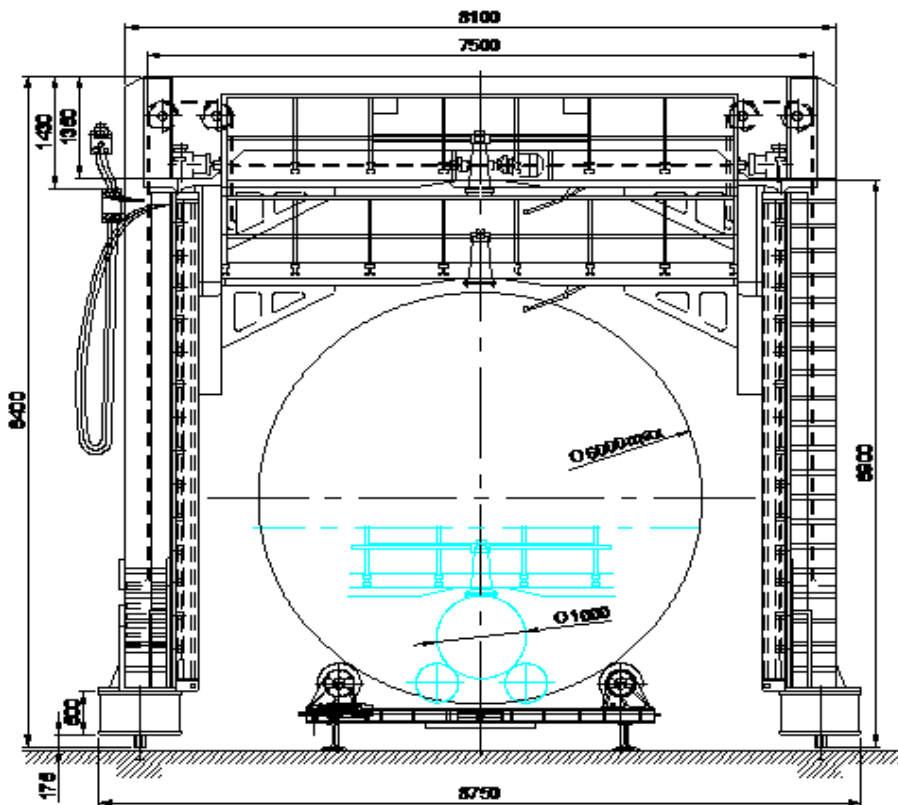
Установка із порталним візком для зварювання циліндричних виробів: зеленим кольором показано розташування зварювального трактора
